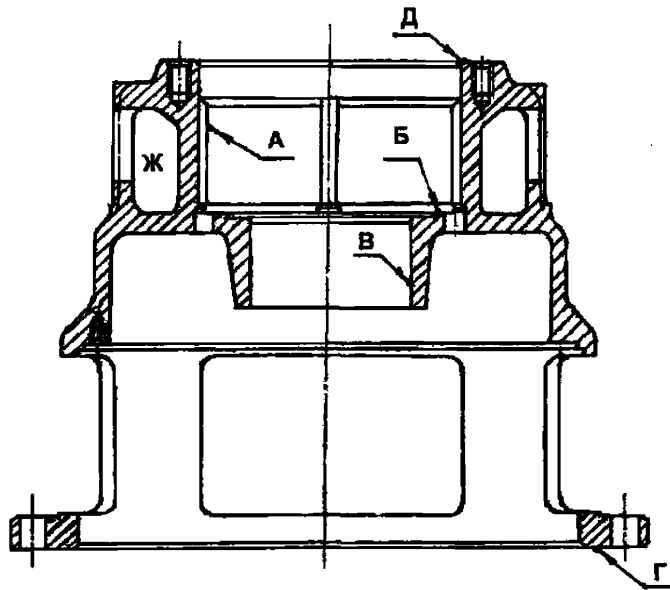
Корпус подшипника (поз. 3, рисунок 57)
